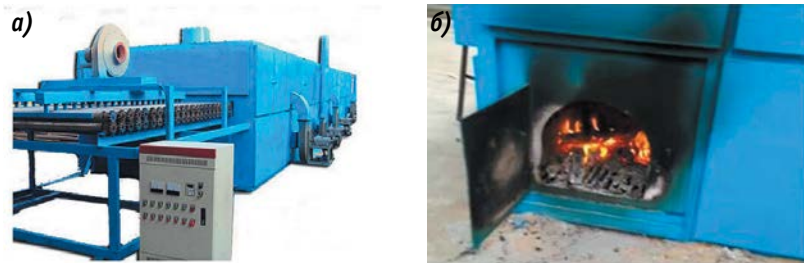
Одноэтажная роликовая сушилка шпона, производитель – фирма Balance Machinery Co., Ltd (а), топка сушилки (б)
